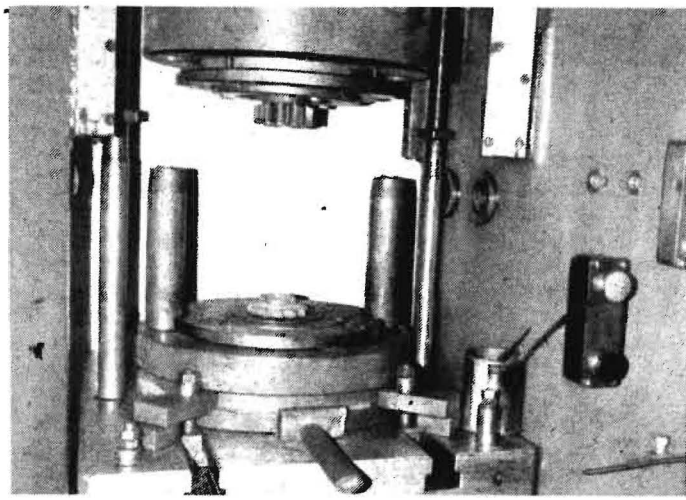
Bogenstatorpresse mit Umformwerkzeugen zur Kettenradumformung mit Kettenrad in Umformausgangsstellung
